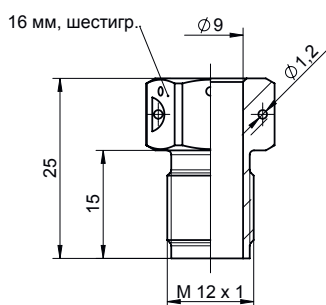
Монтажная гайка M12x1, Тип 6419A21A для датчика с использованием разъема LEMO или свободными концами
